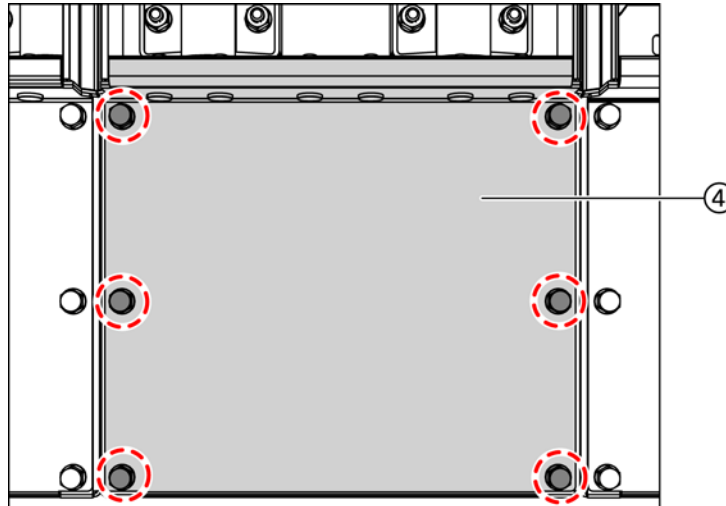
Монтаж поперечной стенки (R-ячейка)
